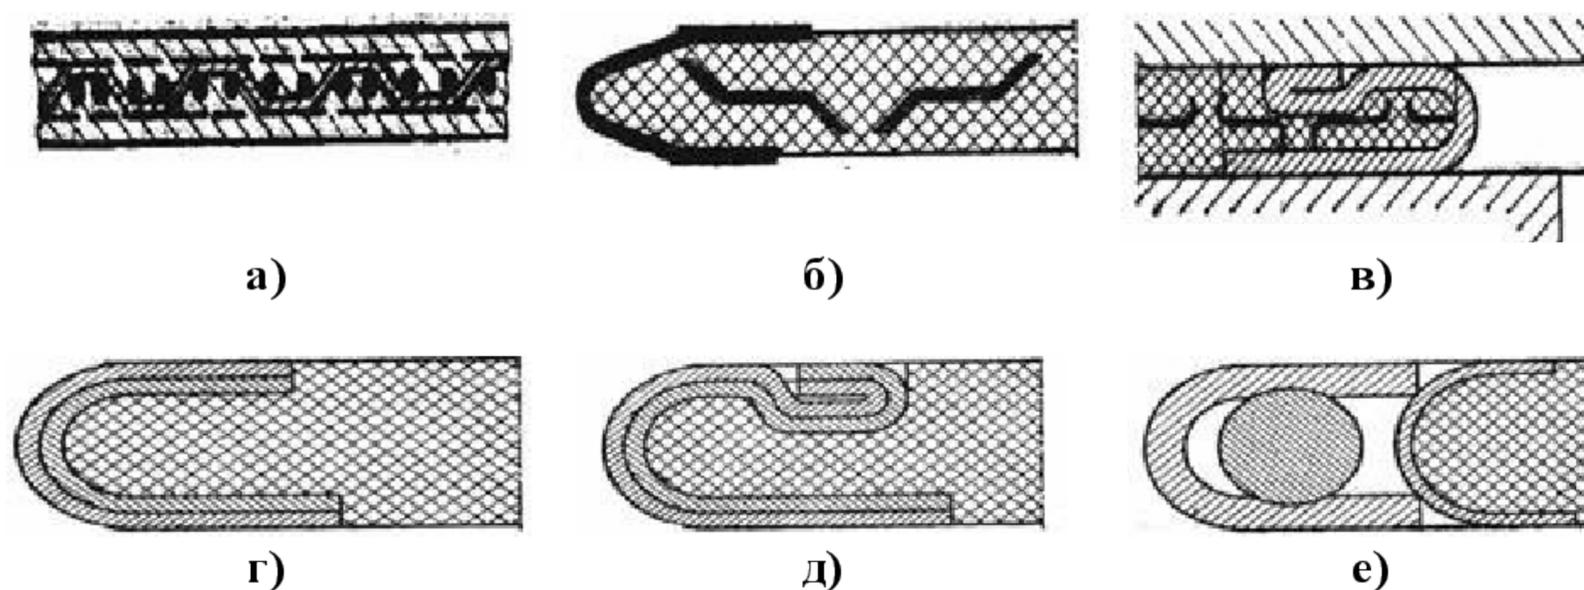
Прокладки для уплотнения газового стыка двигателей
